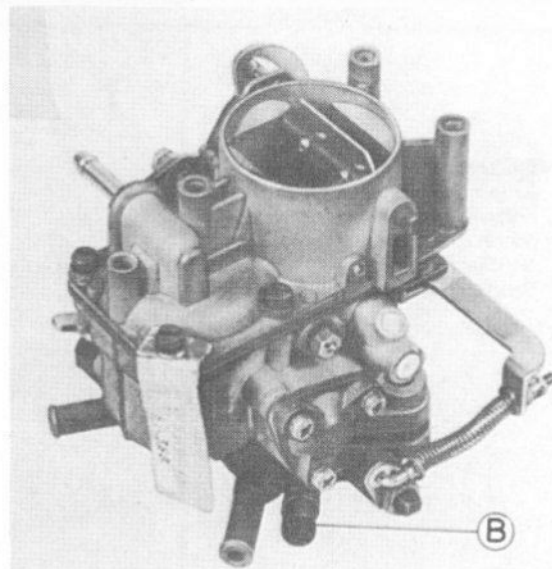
Vis de réglage de richesse (B) des carburateurs Solex 32 et 34 PBISA (Sec 10)
